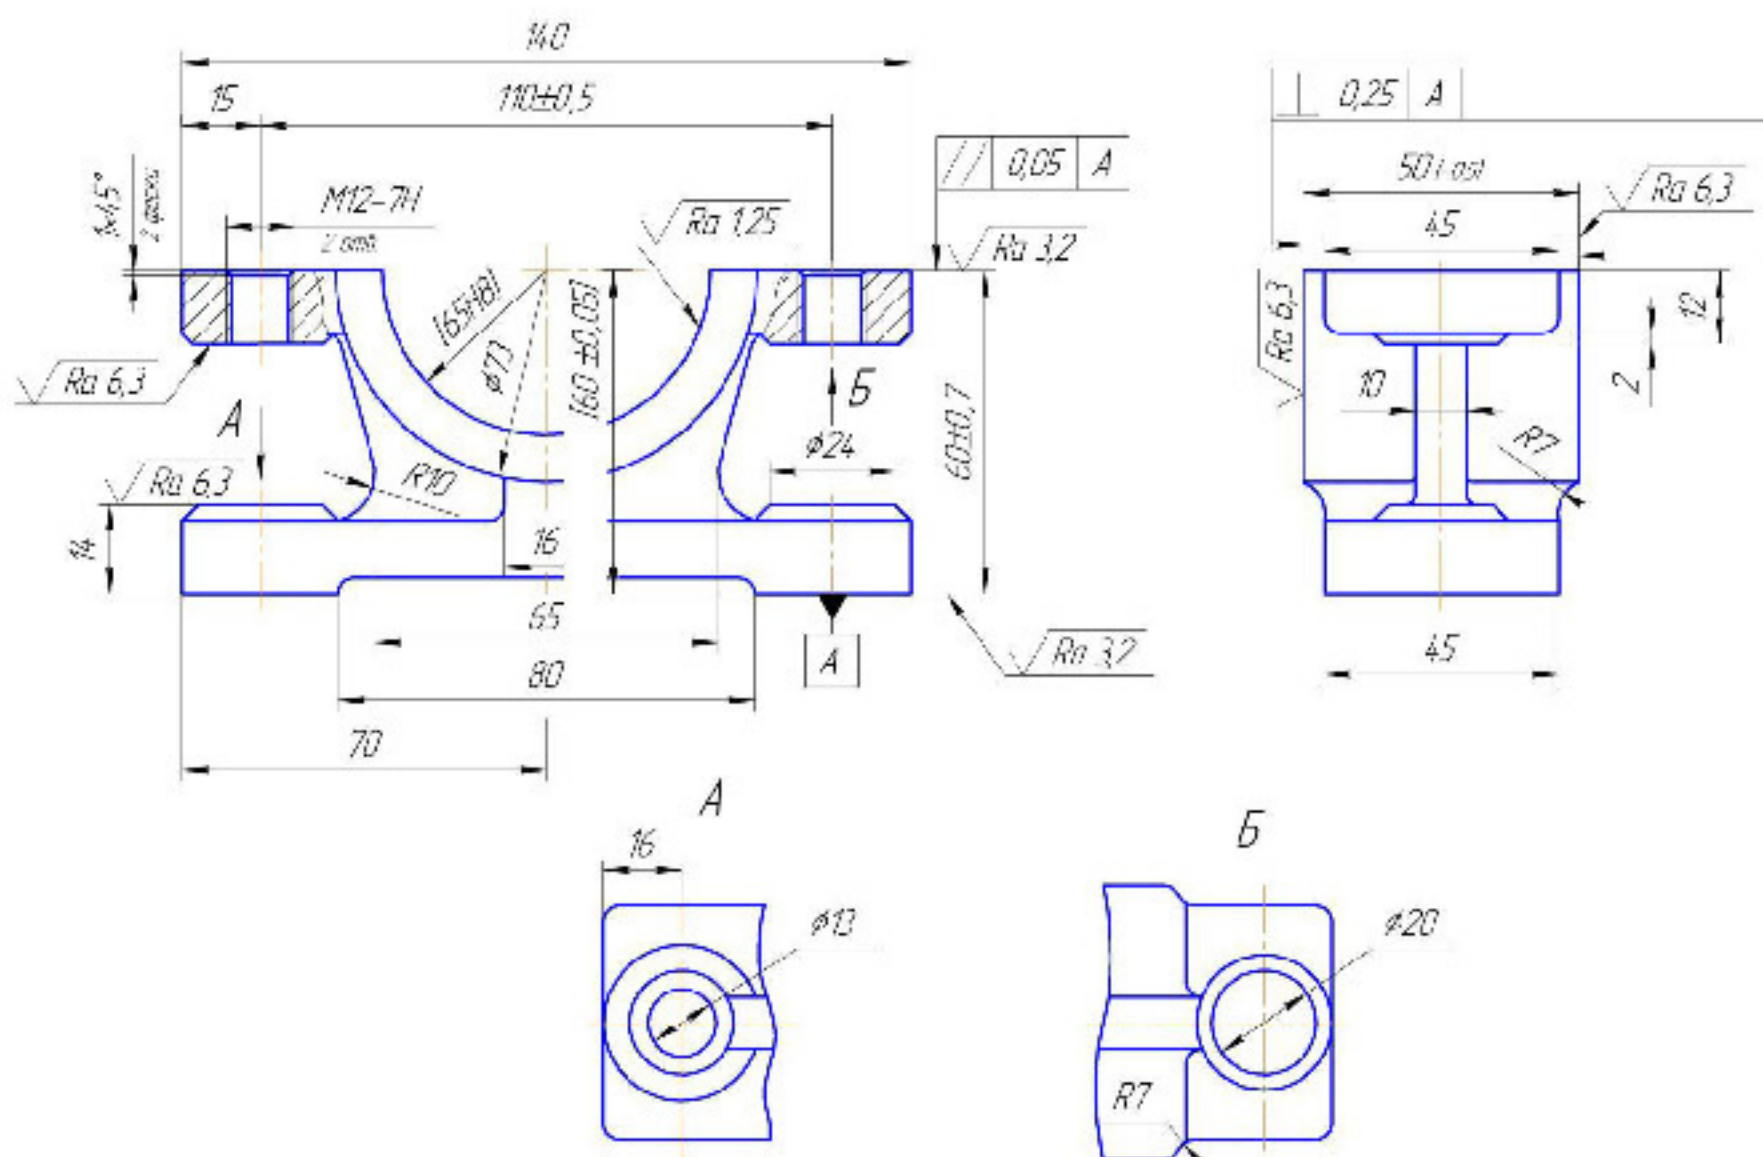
Креслення деталі «Корпус 46.90.001»
